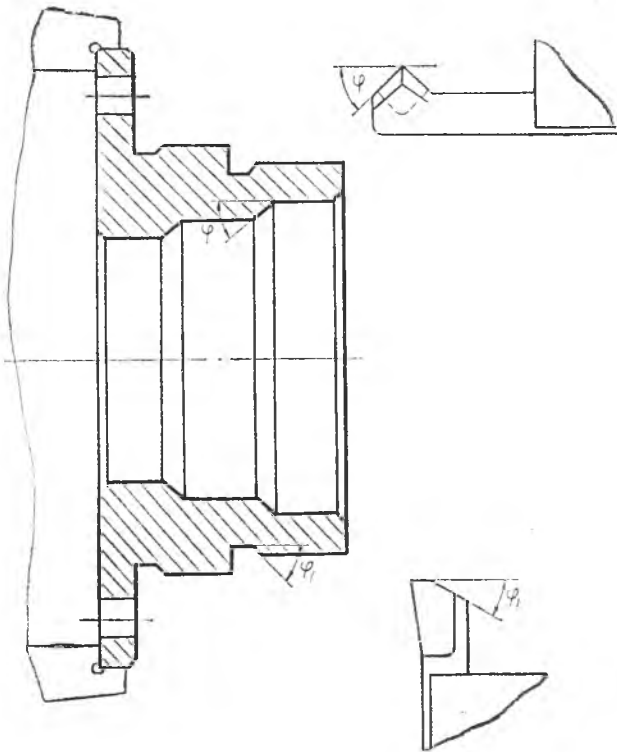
Схема обработки наружной и внутренней поверхности детали при одной установке двумя резцами.
